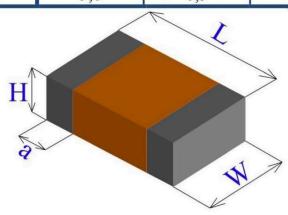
Габаритный чертеж корпуса SMD чип-радиокомпонента и его конструктивные размеры.
